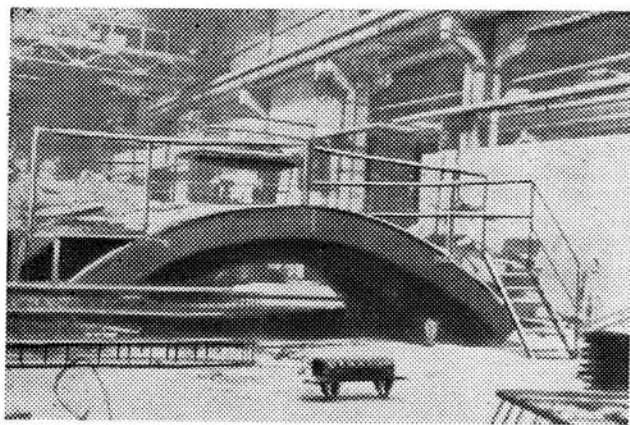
Форма для изготовления тюбингов LP и LP¹
